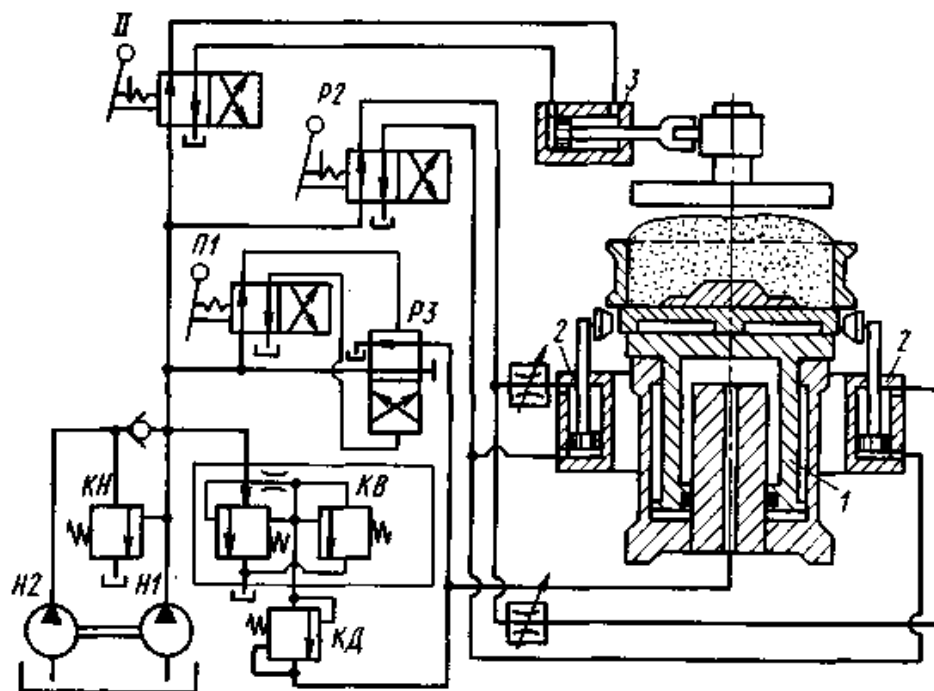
Гидропривод прессовой формовочной машины с верхним прессованием
